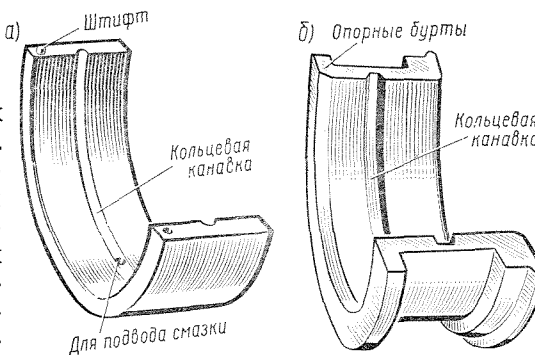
Вкладыши коренных подшипников коленчатого вала дизелей типа Д100: а — опорного подшипника; б — опорно-упорного подшипника
